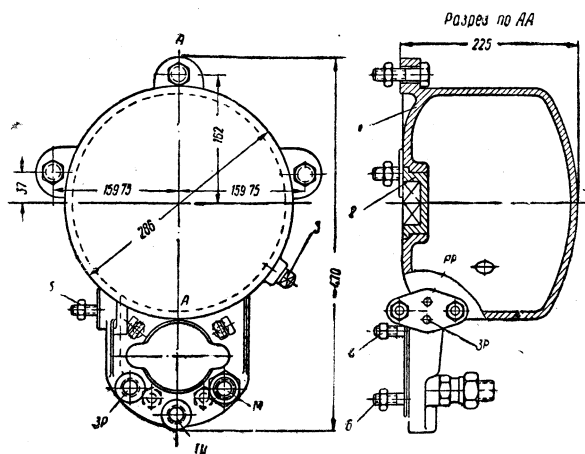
Однокамерный рабочий резервуар усл. № М-Ф1
